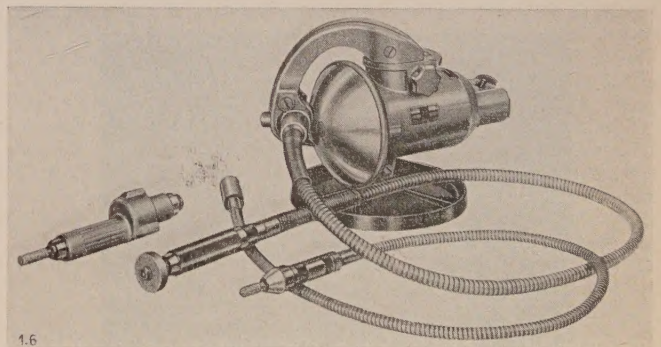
Universal-Schleifmaschine mit biegsamer Welle und stufenloser Drehzahleinstellung.
